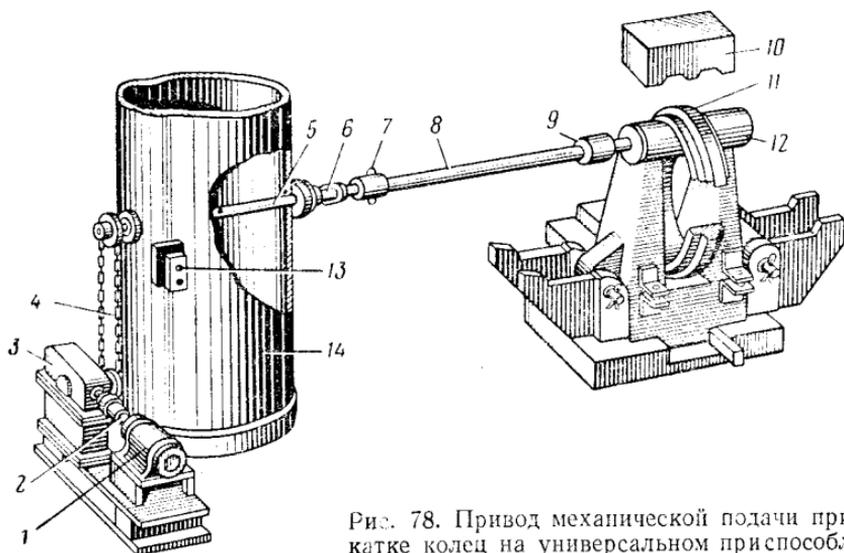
Привод механической подачи при раскатке колец на универсальном приспособлении:
